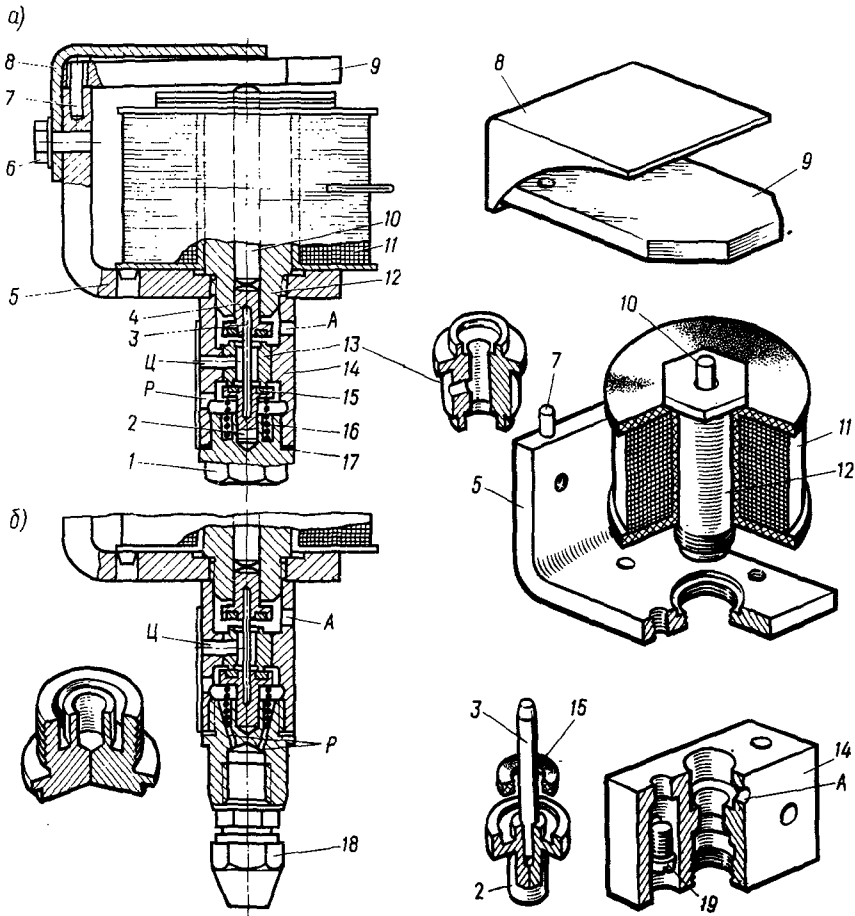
Электропневматический вентиль типа EV51 (а) и нижняя часть вентиля типа EV51/11 (б): 1 — пробка; 2, 4 — впускной и выпускной клапаны; 3 — игла; 5 — ярмо; 6 — болт; 7 — штифт; 8 — упорная скоба; 9 — якорь; 10 — латунный стержень; 11 — катушка; 12 — сердечник; 13 — втулка; 14 — корпус; 15 — резиновое кольцо; 16 — выключающая пружина; 17 — резиновая прокладка; 18 — штуцер; 19 — винт; А, Р, Ц — отверстия для прохода воздуха
